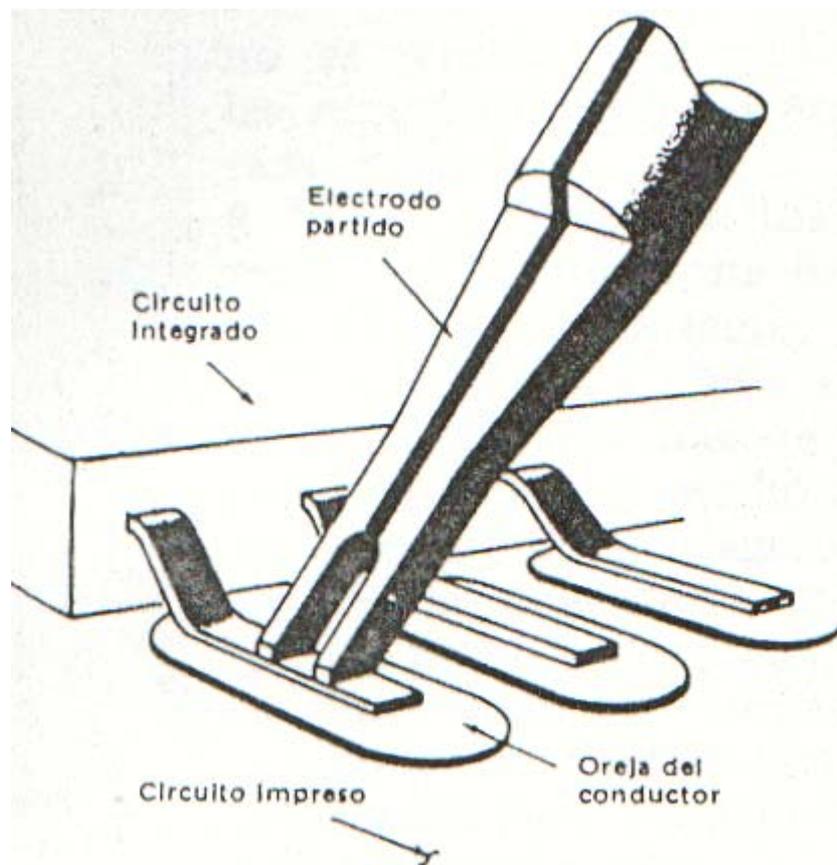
Disposición del Electrodo Partido usado para Soldadura sobre Circuitos Impresos.
